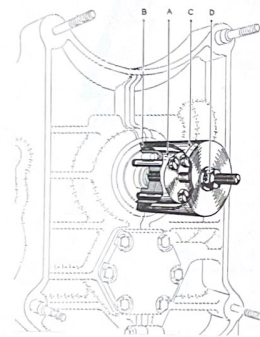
Util 3004-T para la colocación del retén trasero del cigüeñal.
